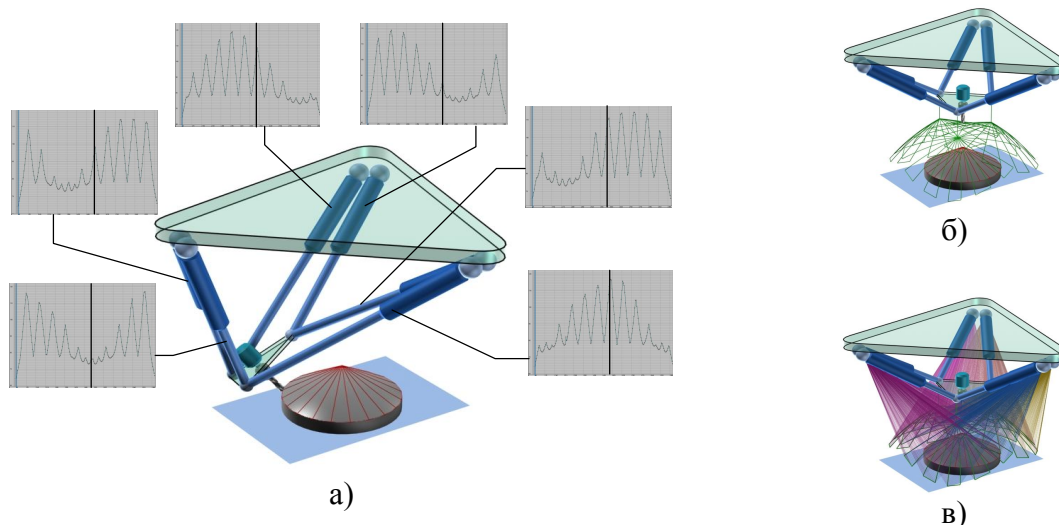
Моделювання обробки верстатом-гексаподом фрезеруванням конічної поверхні по меридіанах: а) графіки змін довжини кожної штанги; б) траєкторії руху шарнірів рухомої платформи; в) сліди штанг гексапода при заданому циклі обробки
